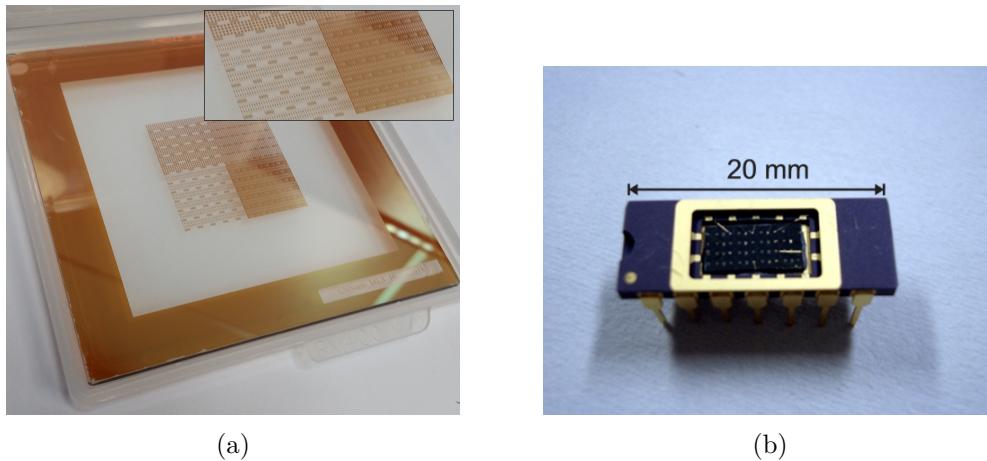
(a) Máscara desenvolvida pelo grupo para a criação de padrões de mesas e contatos na estrutura. (Imagem inserida) *Zoom* nos padrões para criação dos contatos e mesas; (b) Amostra com os contatos soldados no *chip carrier*. Cada mesa quadrada de $0.4 \times 0.4 \text{ mm}^2$ corresponde a um fotodetector.
